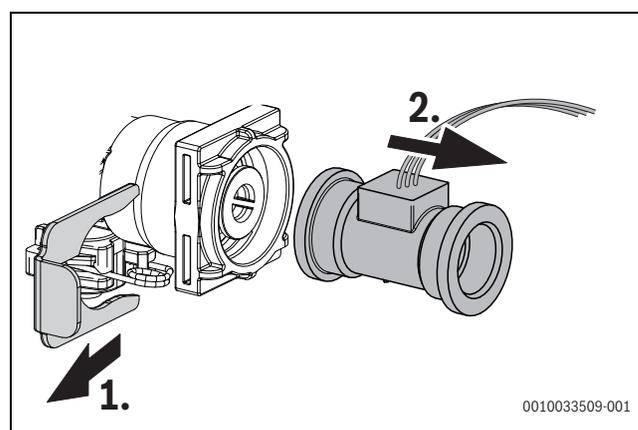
Démontage de la turbine sur le tuyau d'eau froide
